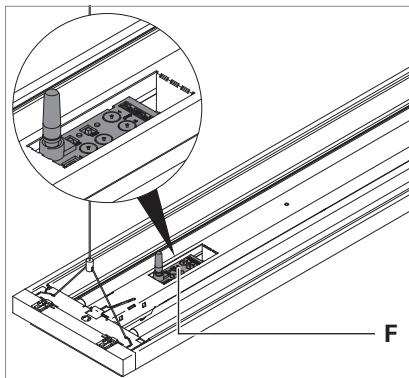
Modulo radio in un apparecchio d'illuminazione a sospensione TYCOON a 2 luci.
